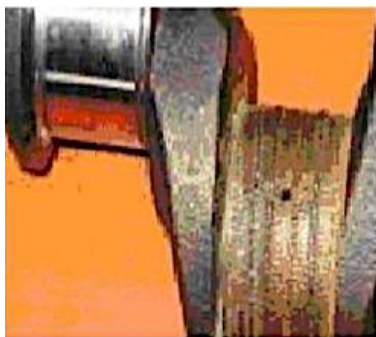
Наваренная шатунная шейка коленчатого вала ДВС
